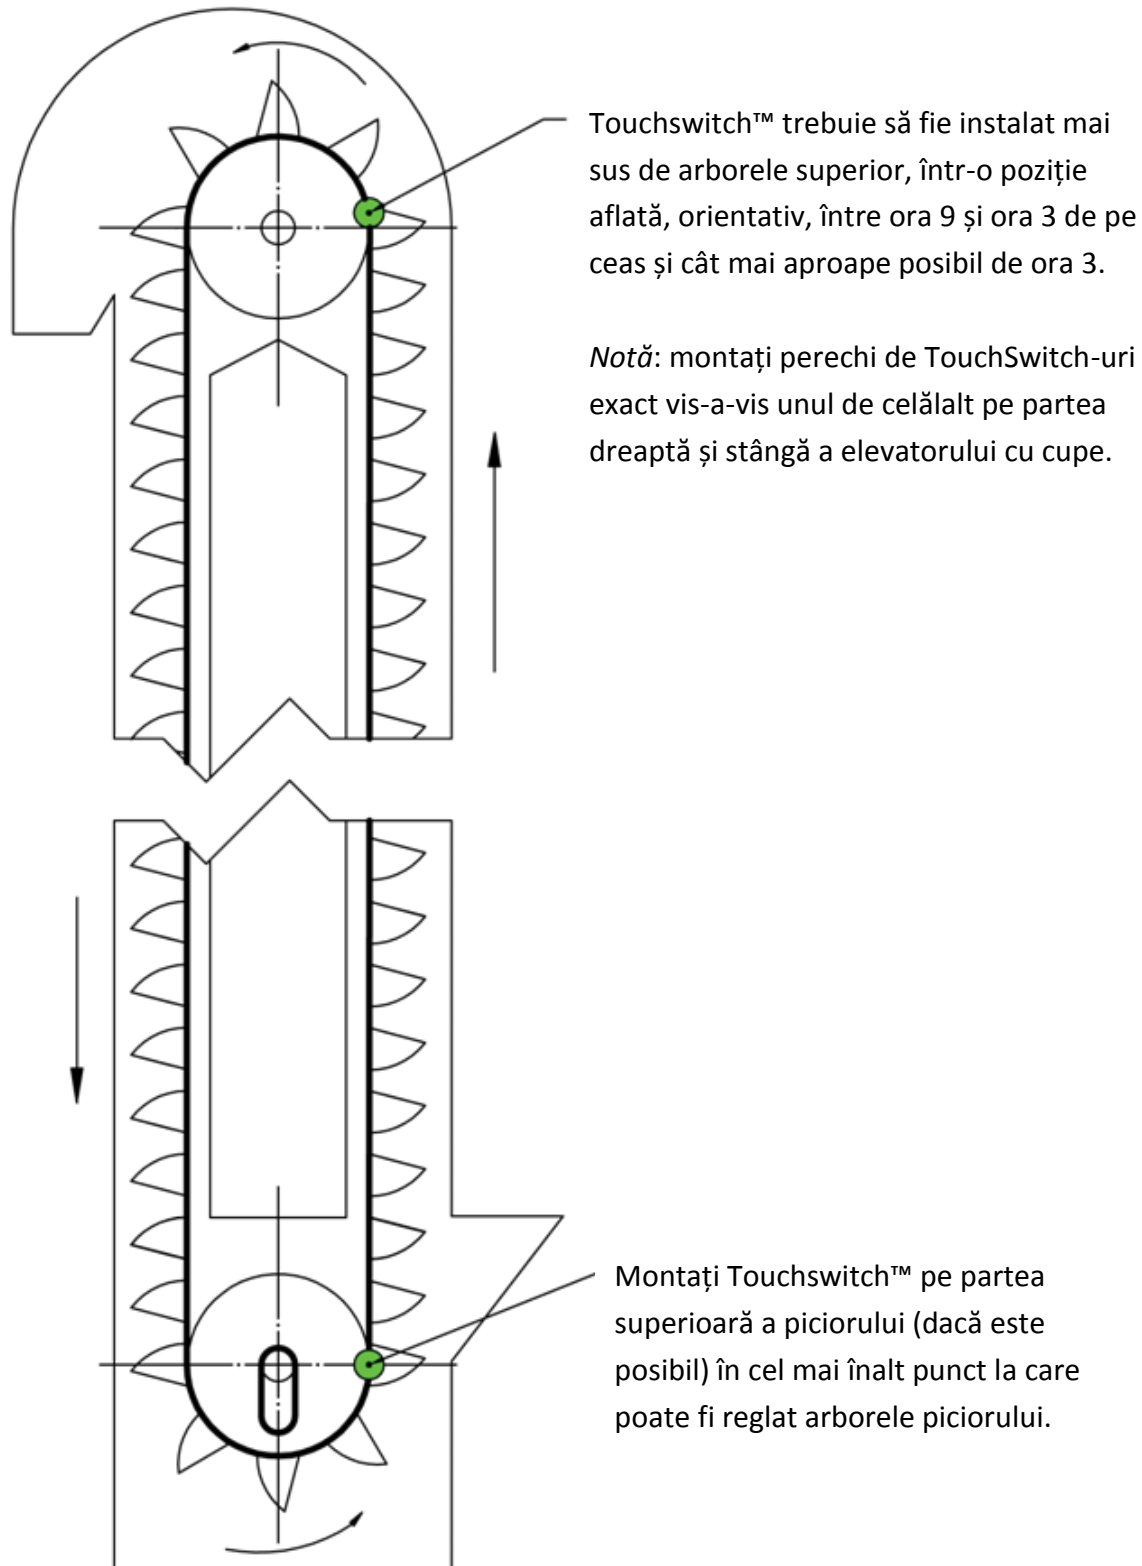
Poziții de montare a Touchswitch – Piciorul elevatorului
